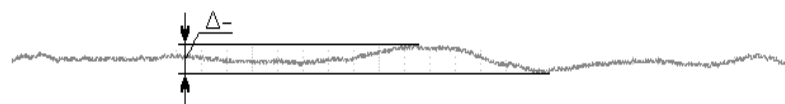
Профиліграмми оброблених поверхностей після зустрічного циліндричного фрезерування з різними частотами обертання шпинделя
